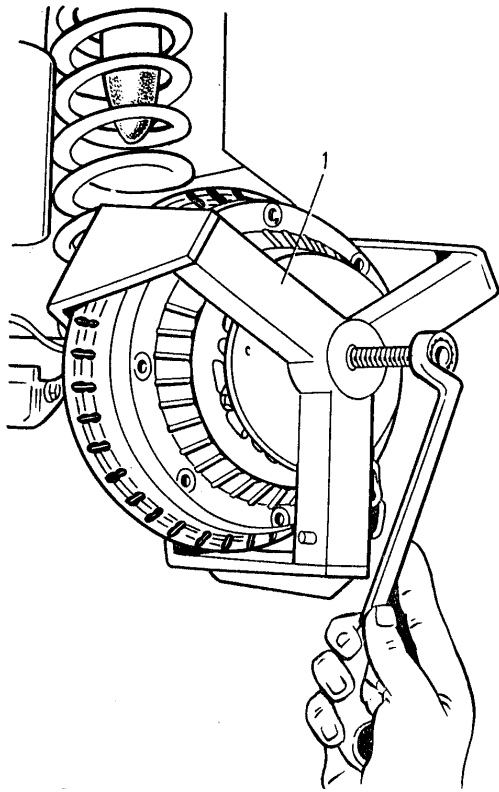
Remoción del tambor de freno: 1- extractor 67.7823.9519
